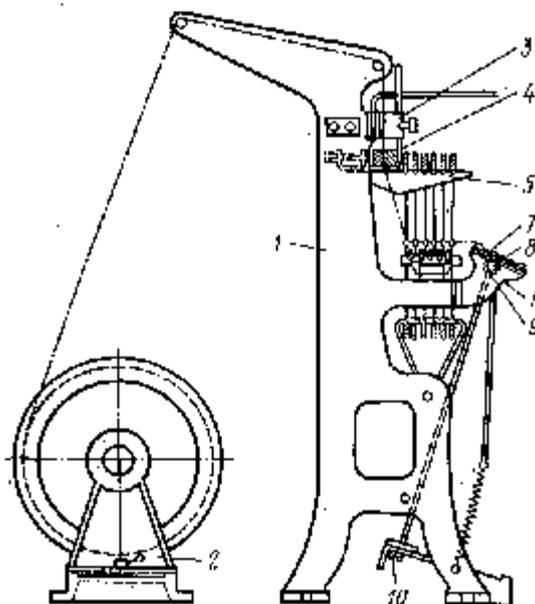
Проборный станок с автоматической подачей нитей в бердо
